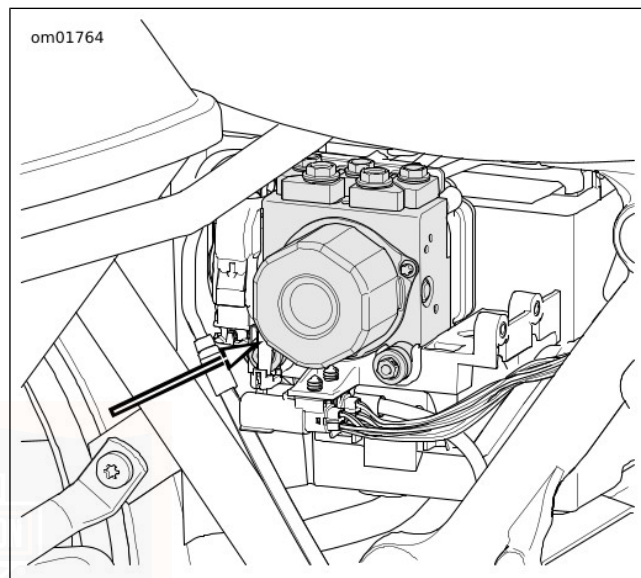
Module ABS (EHCU) (derrière le couvercle latéral droit).
